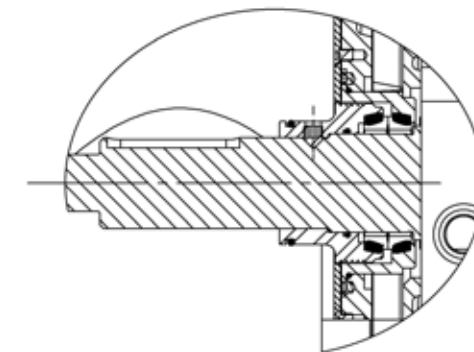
Assemblaggio finale tenute meccaniche.
